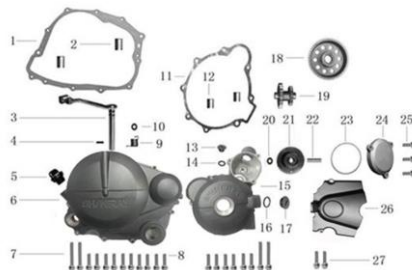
CLUTCH, PLANTA Y MOTOR DE ARRANQUE
